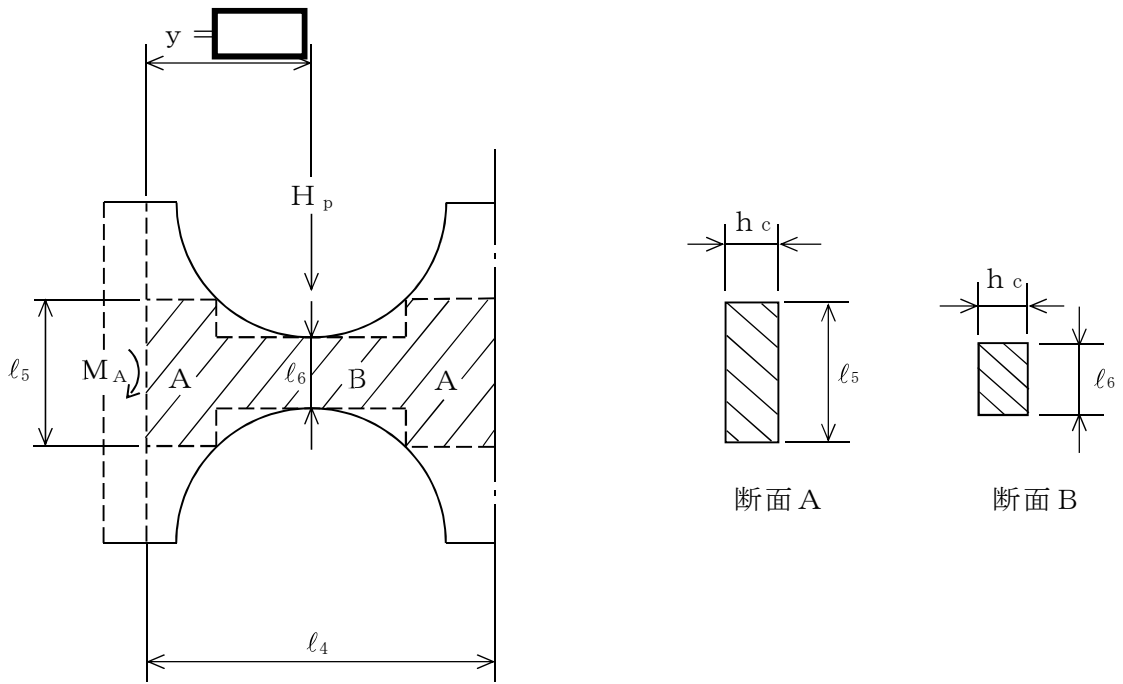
(2) 補強ビームの応力計算モデル (単位: mm)
